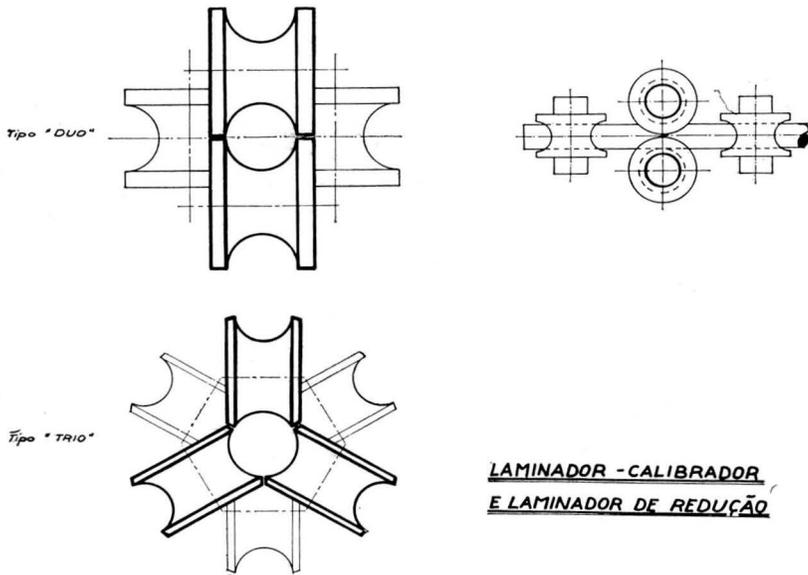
Laminador calibrador e laminador de redução; executam a calibragem exata dos diâmetros do tubo, a quente.
